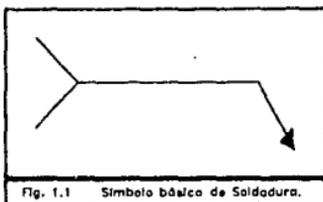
Símbolo básico de Soldadura.
